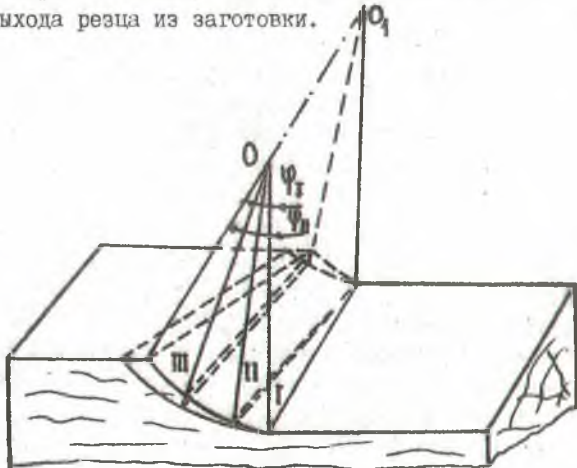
Схема стружкообразования при фрезеровании древесины резцом с углом наклона профиля  $\psi$ .
